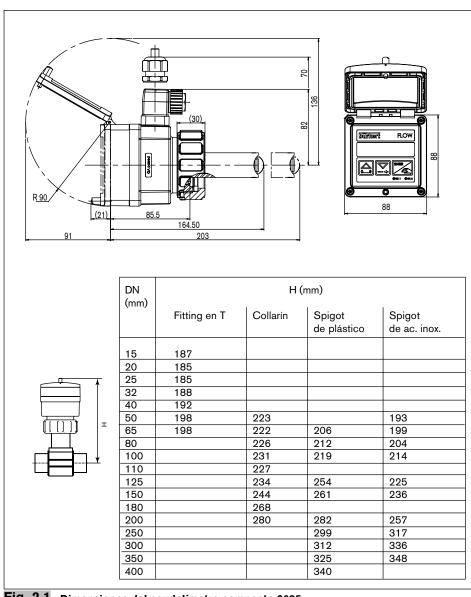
Dimensiones del caudalímetro compacto 8025
